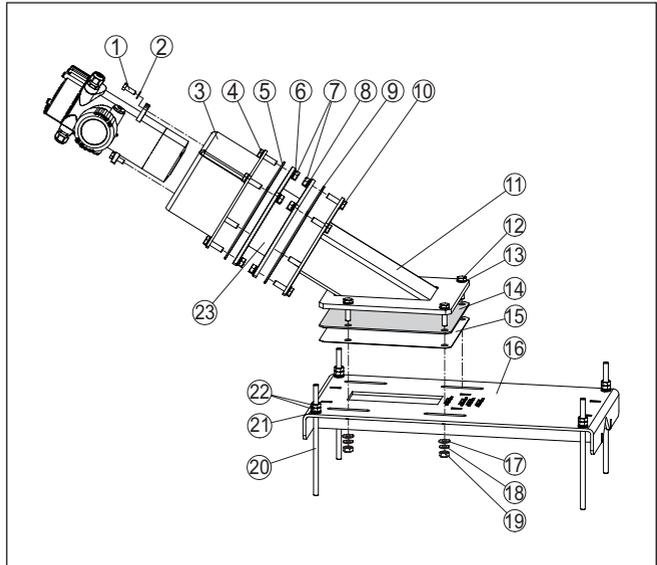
Dispositivo de fixação, lado do sensor (MINITRAC)
